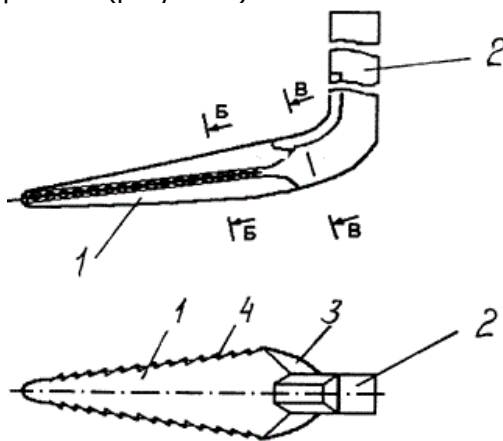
Патент RU2252519C1 общий вид рабочего органа культиватора
